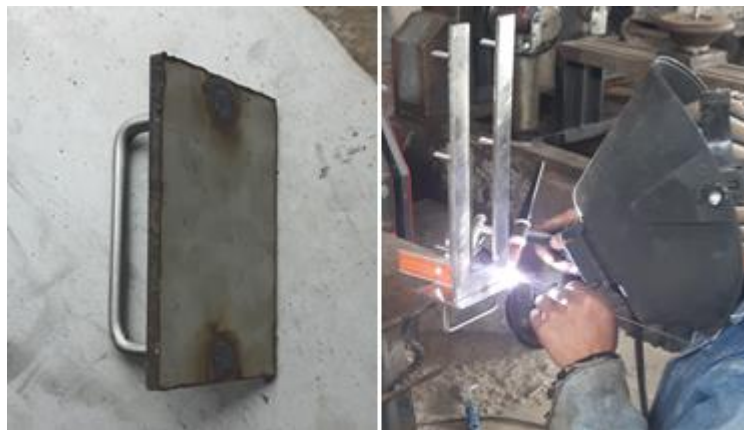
Proceso soldadura TIG ensamble portamuestras.
